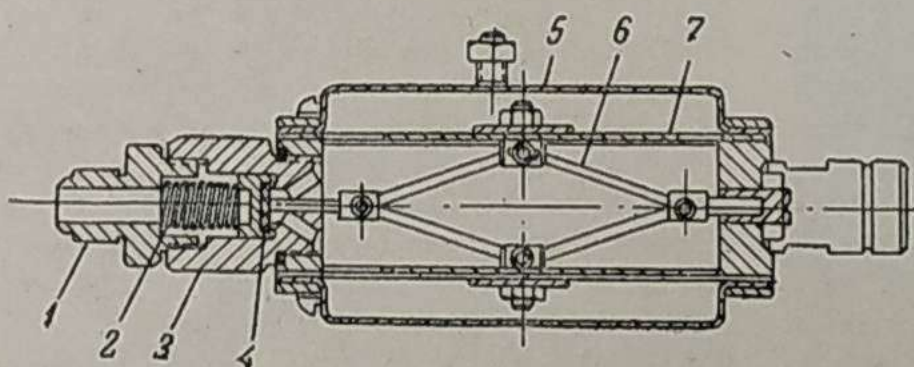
Редуктор низкого давления: 1 — входной штуцер; 2 — пружина редуктора; 3 — переходной штуцер; 4 — клапан; 5 — крышка редуктора; 6 — система рычагов; 7 — мембрана.
